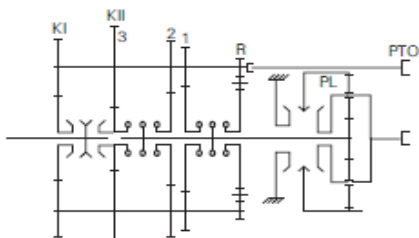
Схема силового потока в коробке передач ZF-AS Tronic с двумя промвалами
